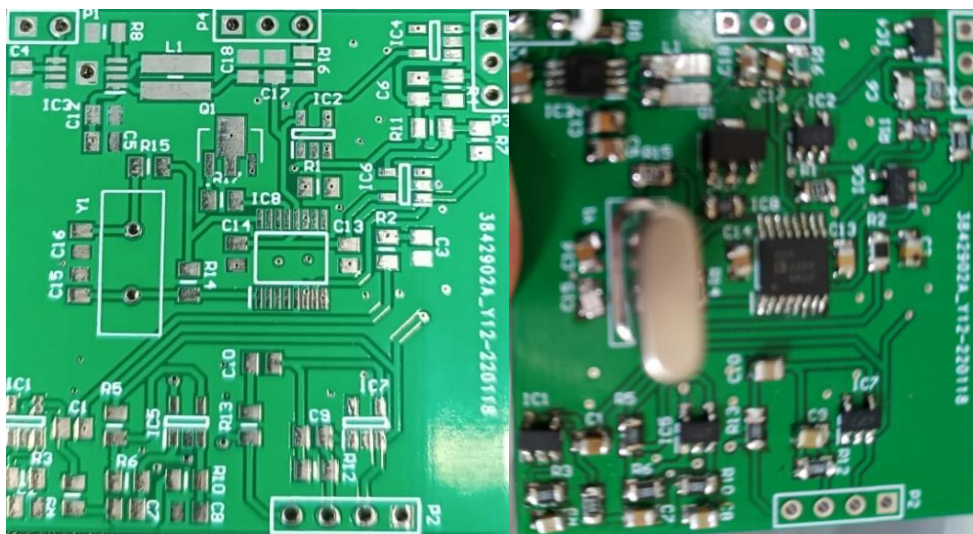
Diferença da PCB com e sem componentes soldados.
